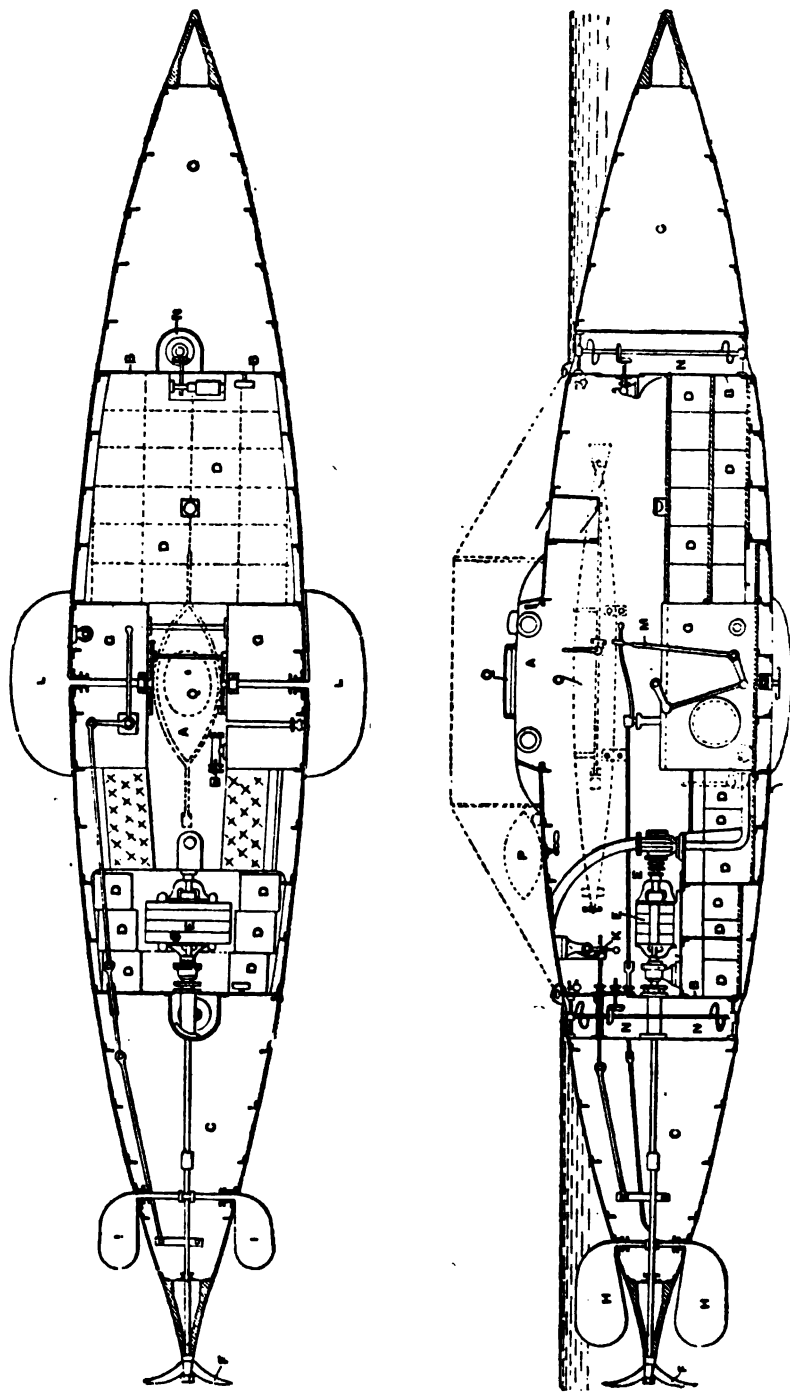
Torpilleur Waddington (plan et coupe longitudinale).
